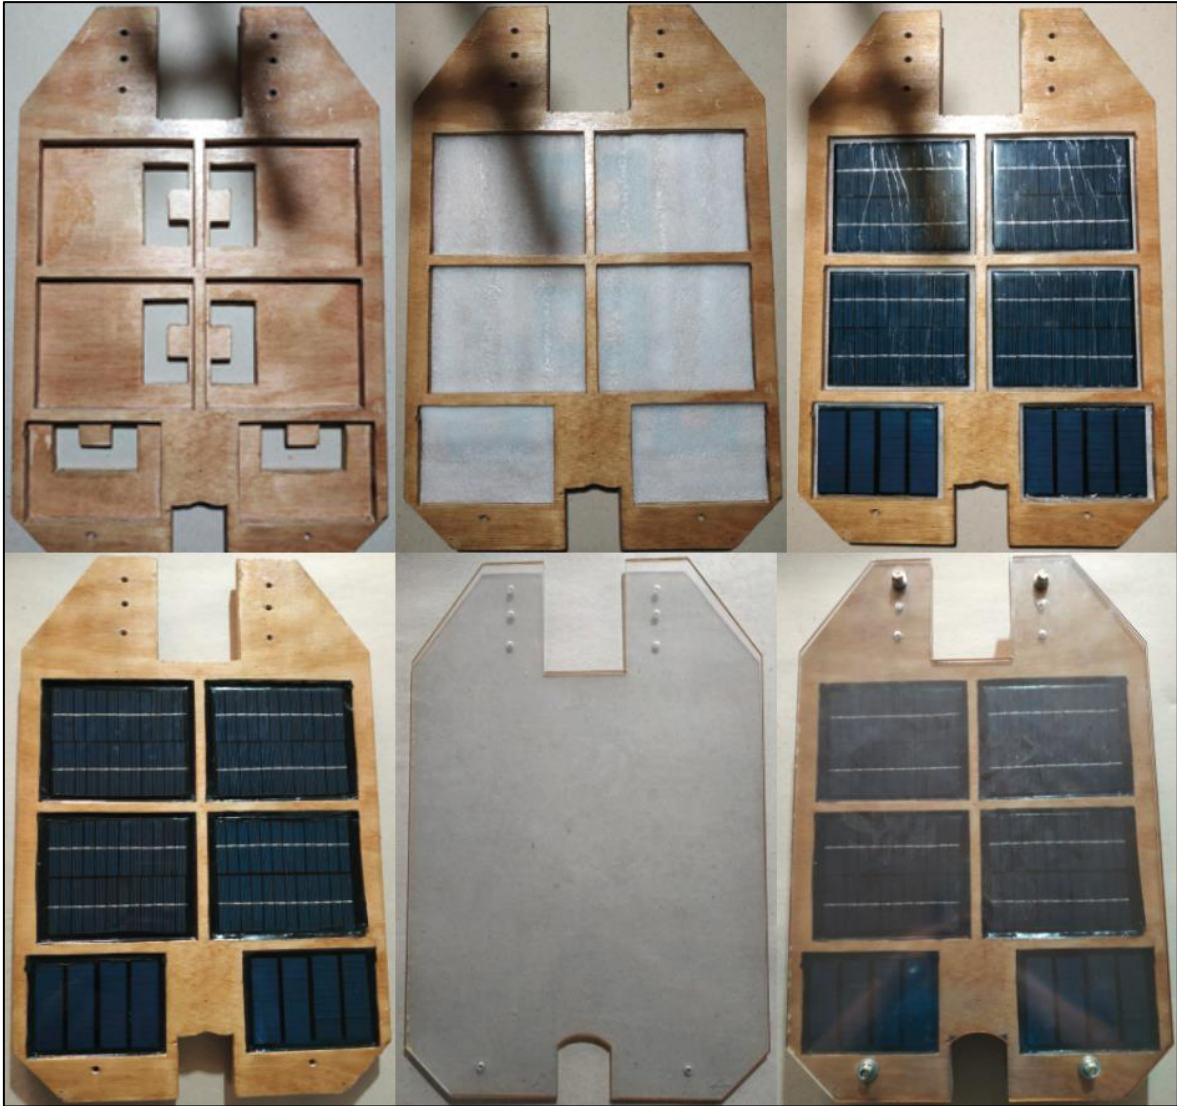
Fabricación y ensamble del panel o módulo fotovoltaico diseñado.
